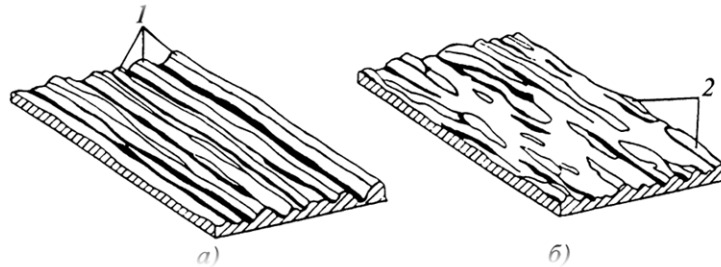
Структура микрорельефа боковых поверхностей зубьев
